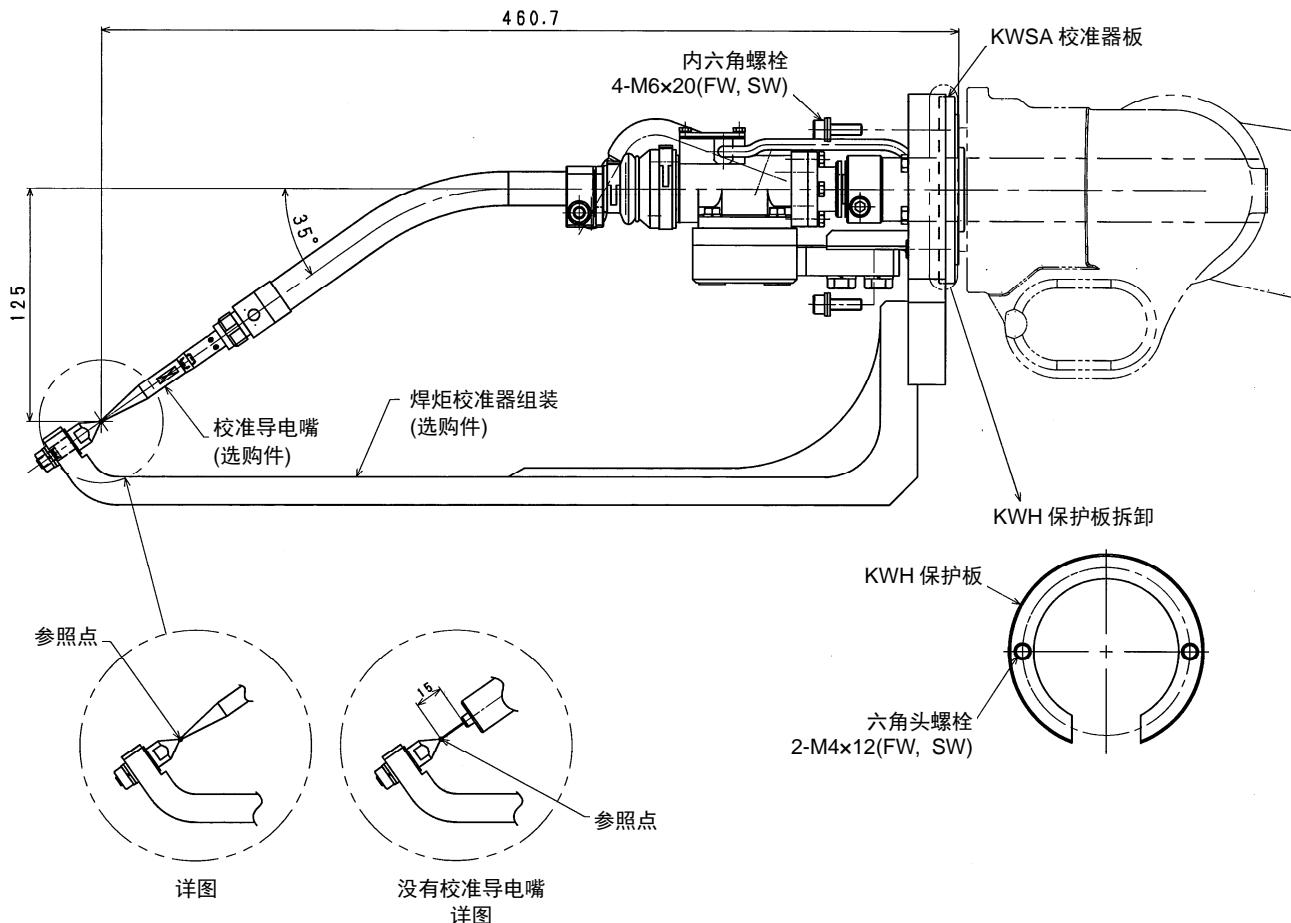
TOKIN 公司生产的焊炬校准器(G-type)(选购件)的安装
